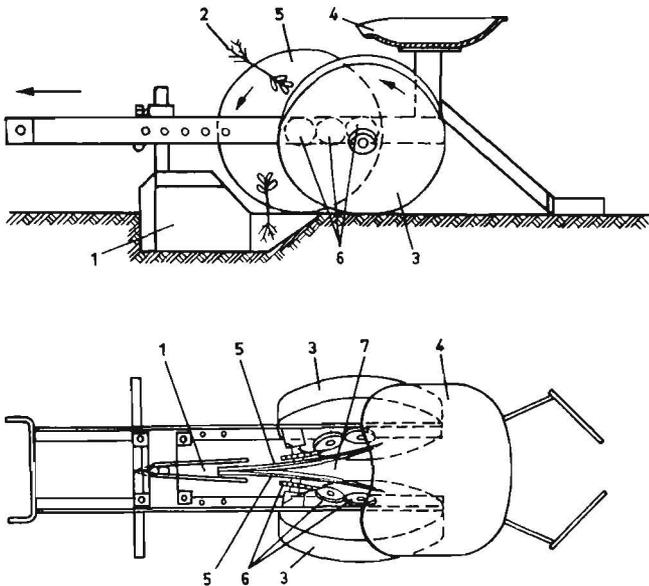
Pflanzsetzmaschine mit Pflanzscheiben, oben in Seitenansicht, unten in Draufsicht (deutsche Patentschrift 923814)
